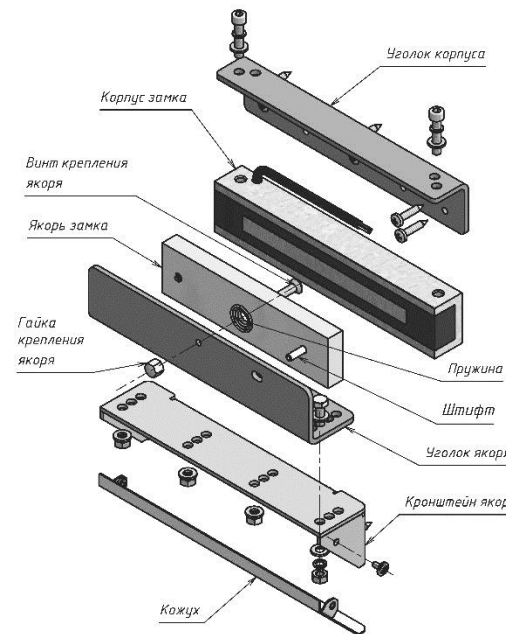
Крепление замка на дверь, открывающуюся вовнутрь
